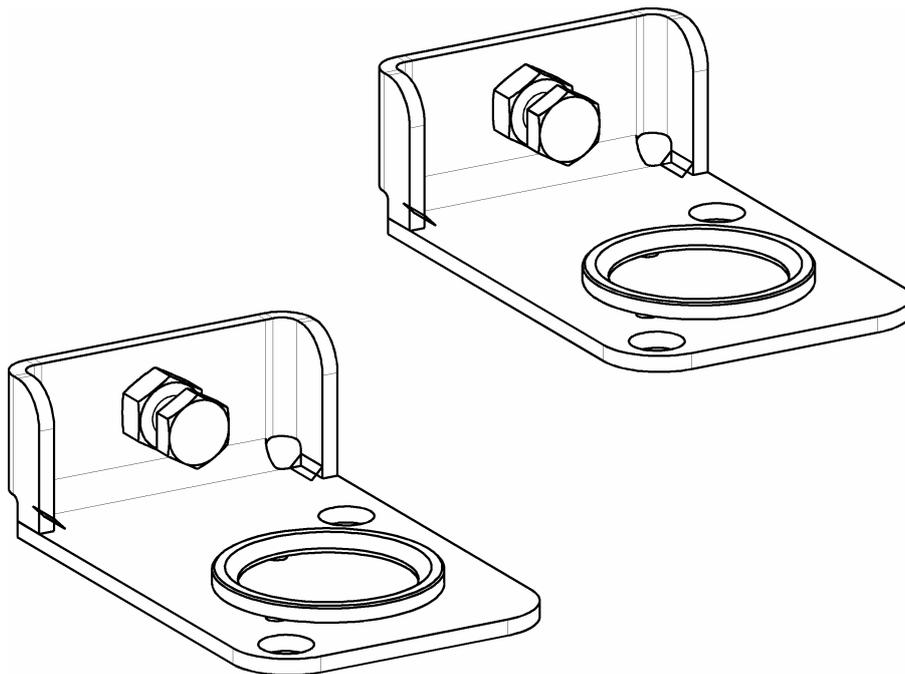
Fußplattenset mit auf Distanz geschweißten Zentrierringen und Anschlagsschrauben
